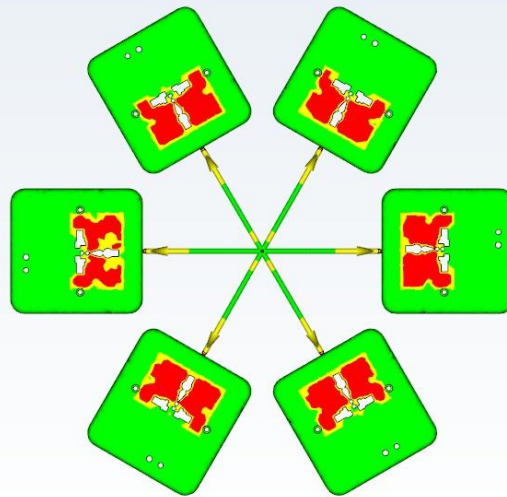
138 Tampak *Explode View Mold Unit* Komponen Terminal Listrik *Inbow
